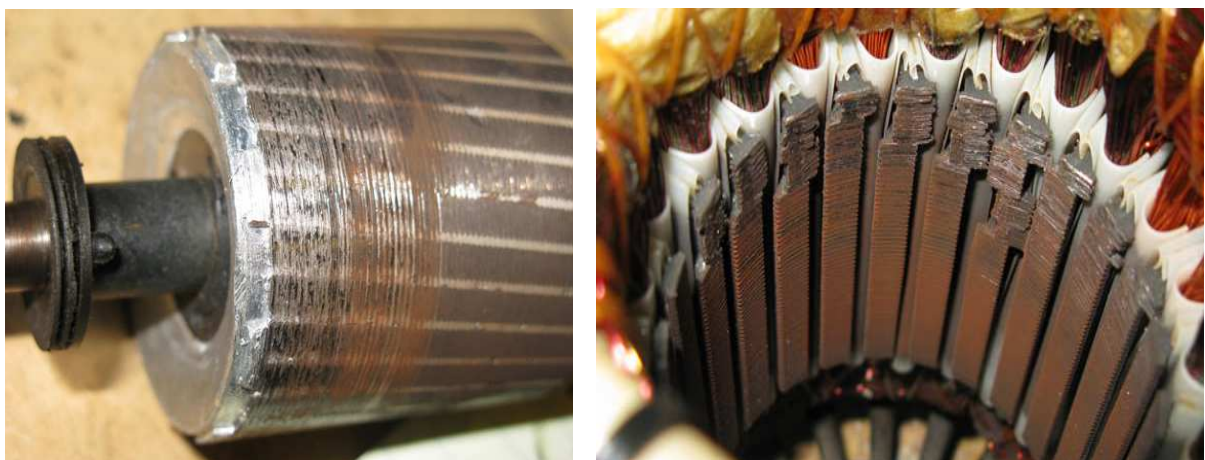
Exemples de dégâts aux stator et rotor dus au défaut de roulement d'un moteur asynchrone.
